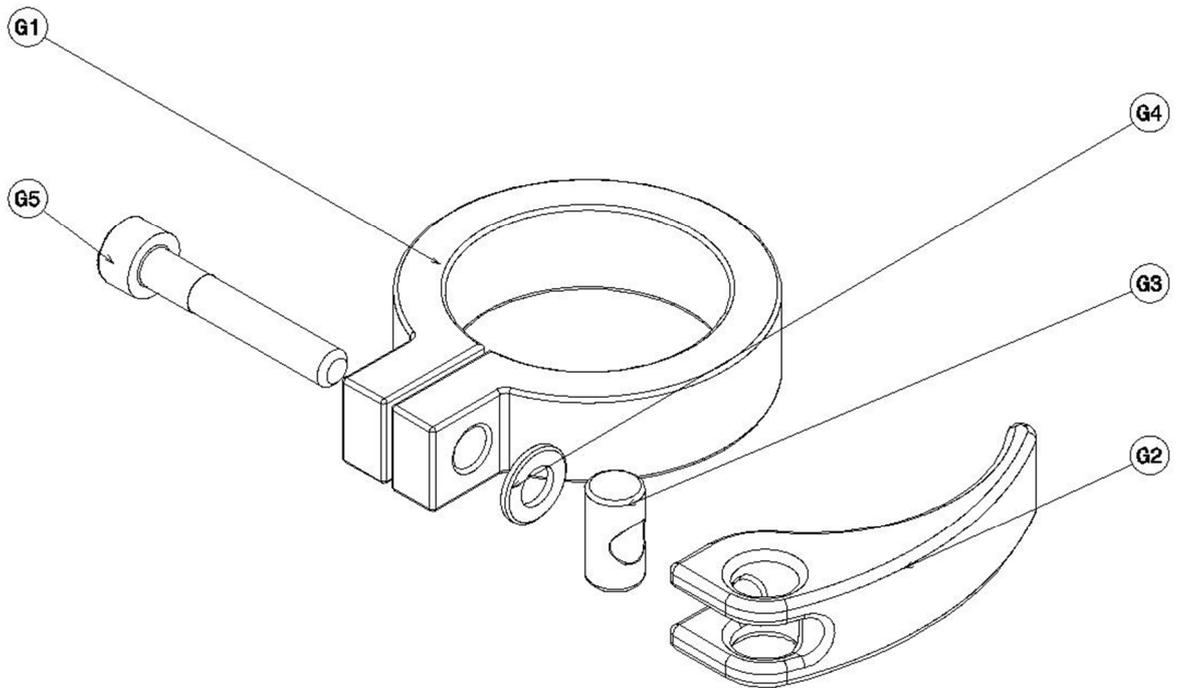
Explosión en vista isométrica del subensamblaje estructura tubular interna.
